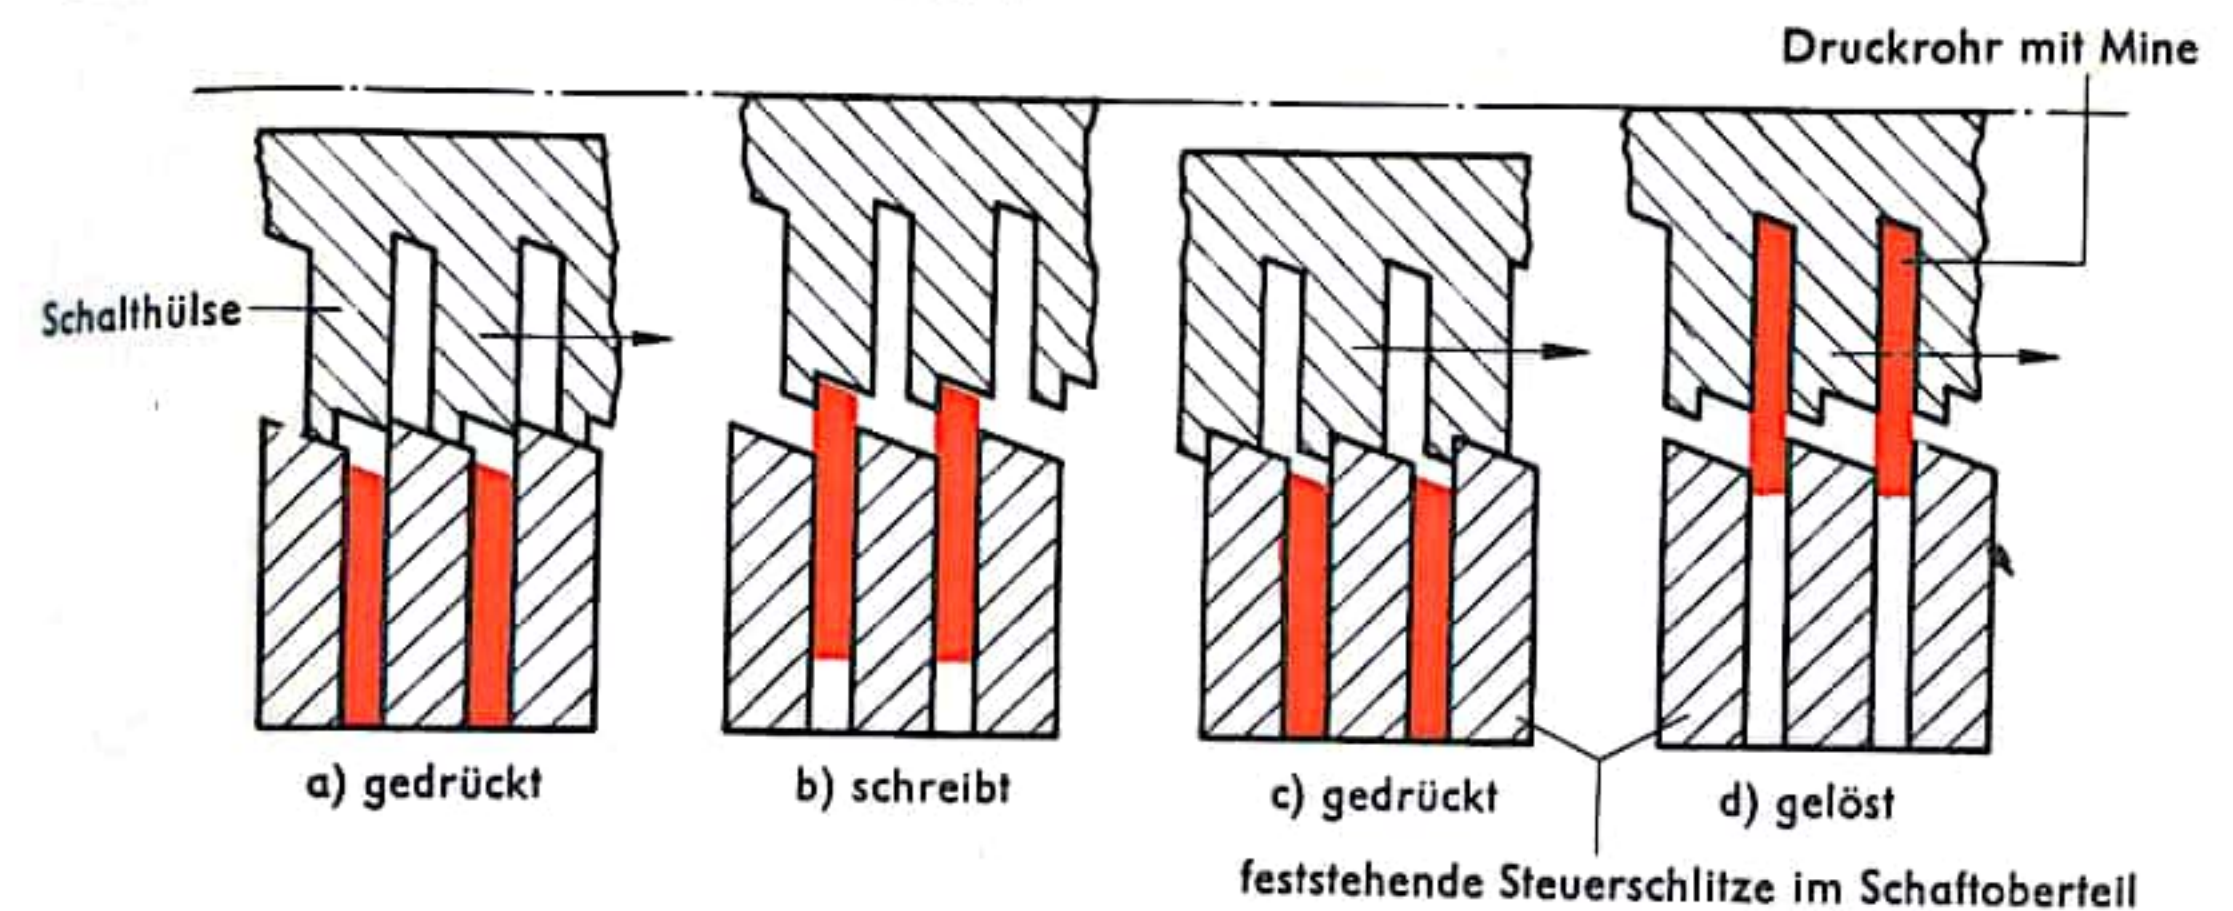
Druckkugelschreiber mit Kugelmechanik
